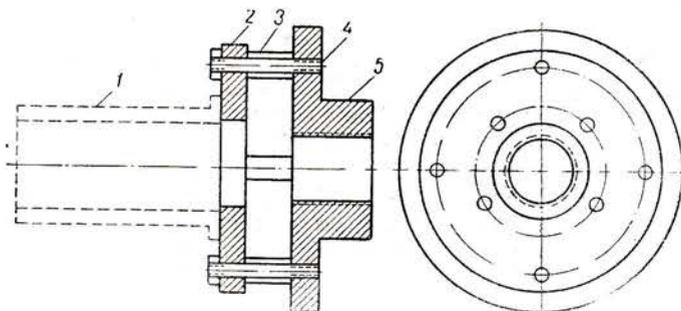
Общий вид приспособления для расточки и шлифовки цилиндра Л-3/2
